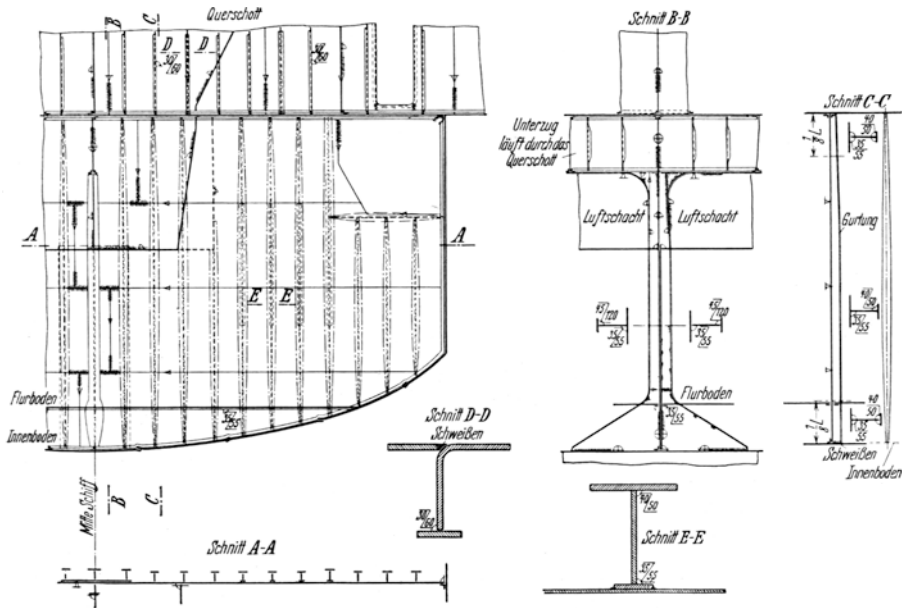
Geschweißtes Querschnitt eines Schlachtschiffs.
